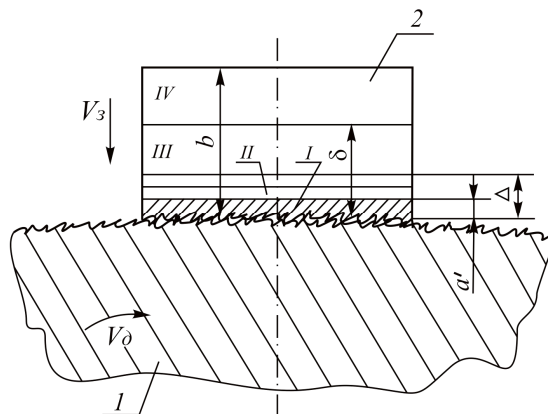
Схема взаимодействия заготовки 2 с передней поверхностью режущего диска 1
